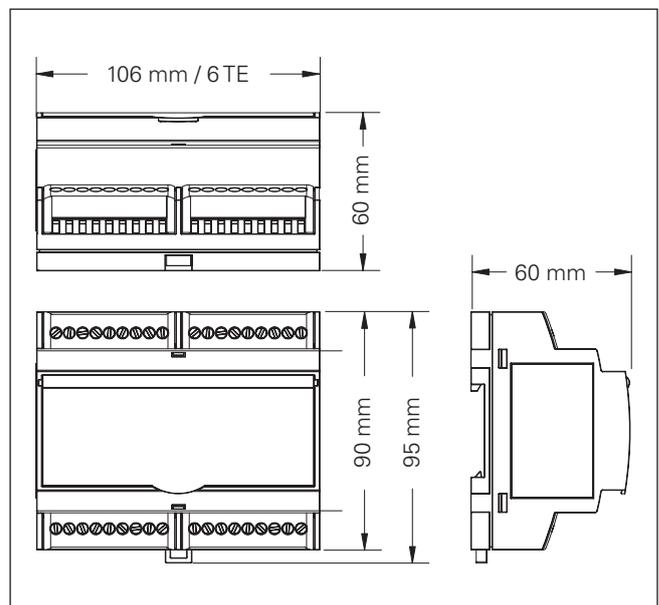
Abmessungen REG-Gehäuse für Dimmkaktor 2D
